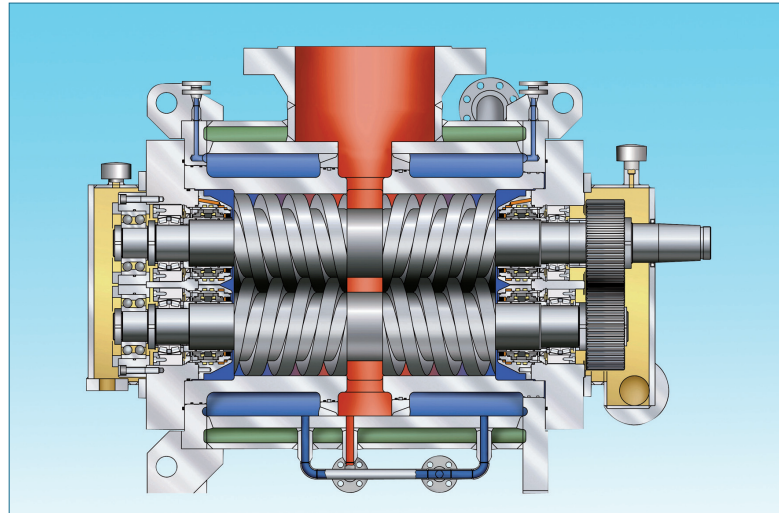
Schnitzzeichnung einer zweispindeligen Multiphasenpumpe
